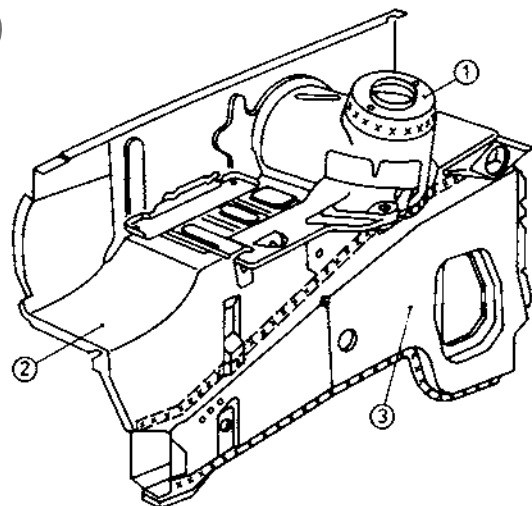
Beispiel: Zusammenbau Radgehäuse vorn; Schweißen Kappe Stoßdämpfer und Längsträger an Stehblech, Werkstoff: Stahlblech St 1201.
